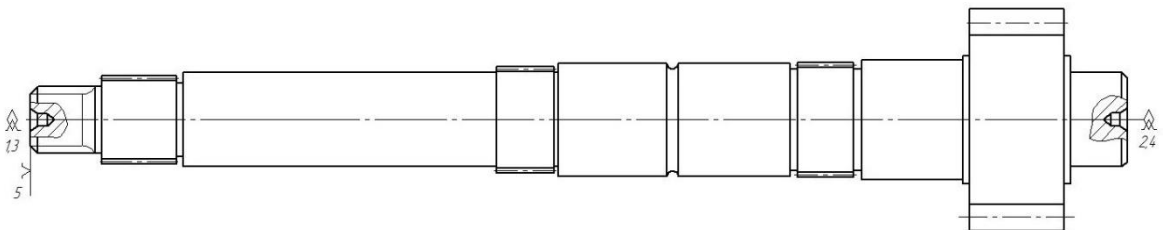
Схема установа вала при шліфуванні опорної шийки з базуванням у центрах.
